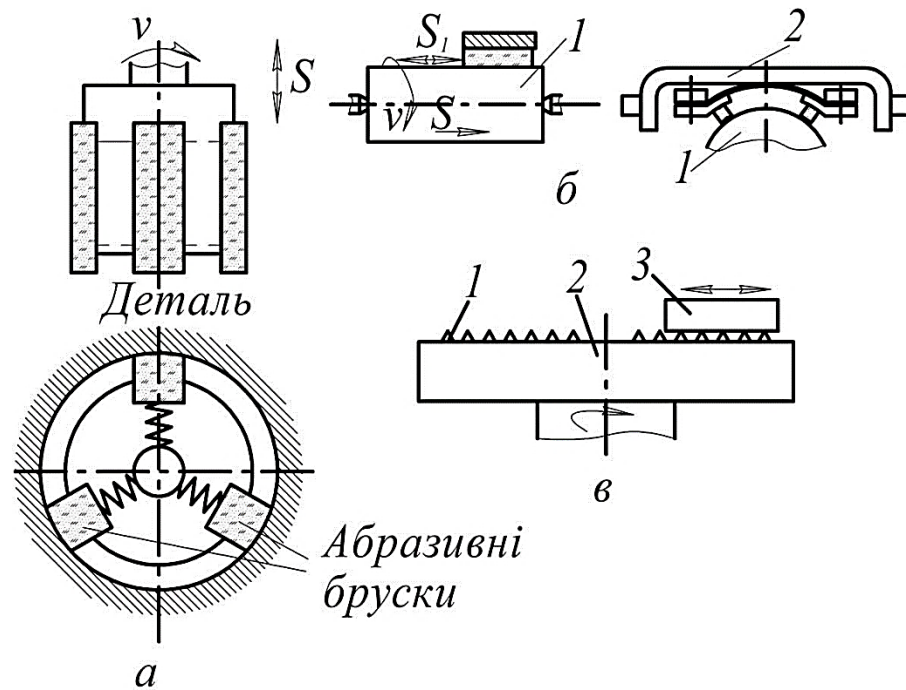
Схеми чистової обробки поверхонь - хонінгування
